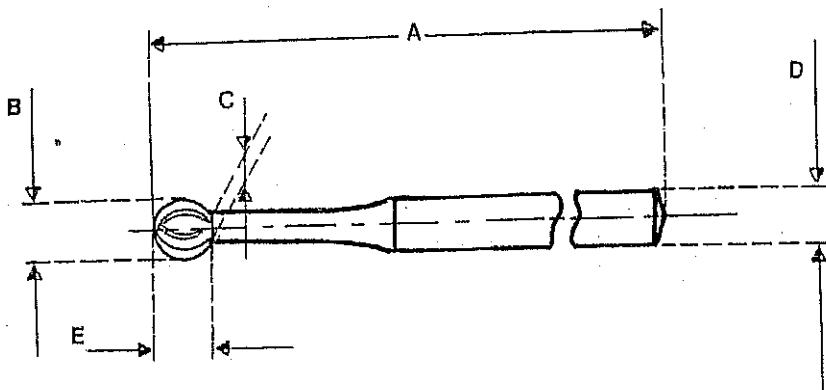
Fresas de carburo, forma redonda (claves: 060.431.0409, 060.431.0417, 060.431.0631, 060.431.0649)
